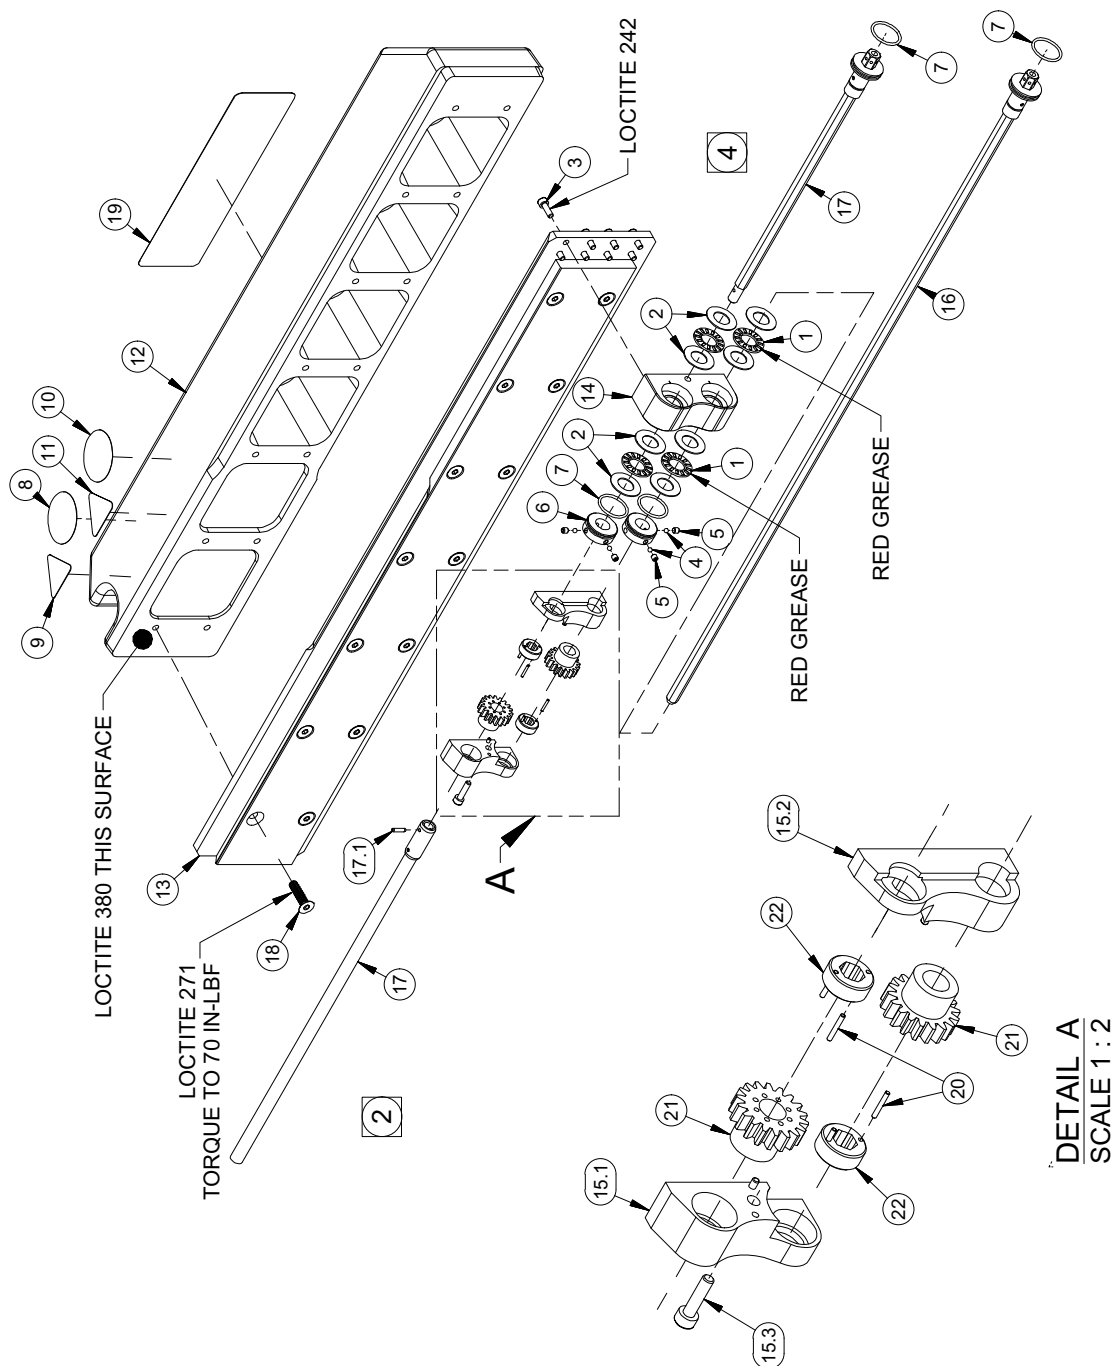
MONTAJE DEL BRAZO DE MECANIZADO (P/N 90337 REVISIÓN E)
